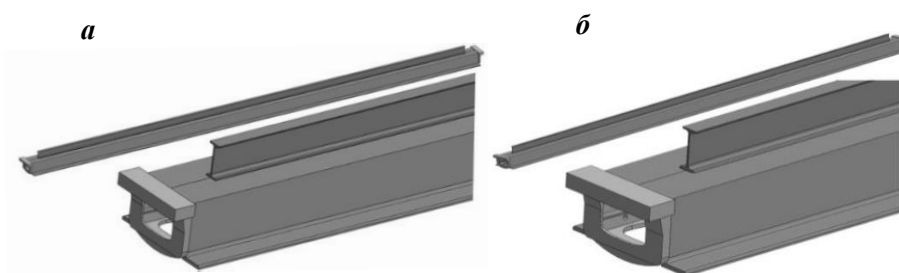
Балка хребтова без зварного шва (а) та із зварним швом (б)
